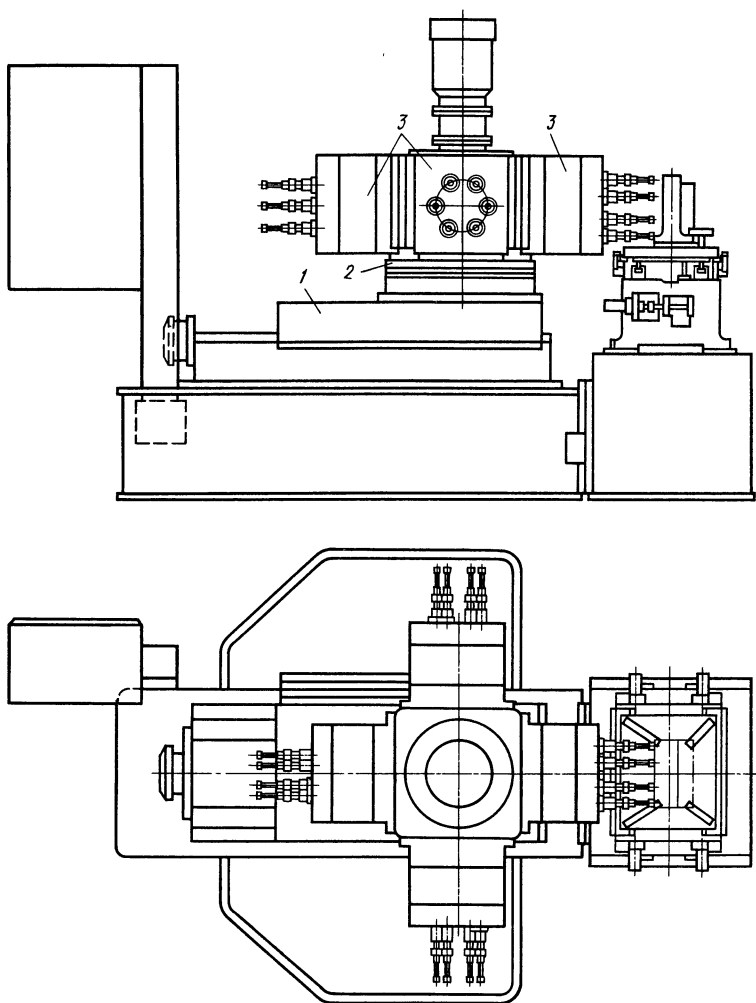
Переналаживаемый агрегатный станок с многшпиндельными коробками:
